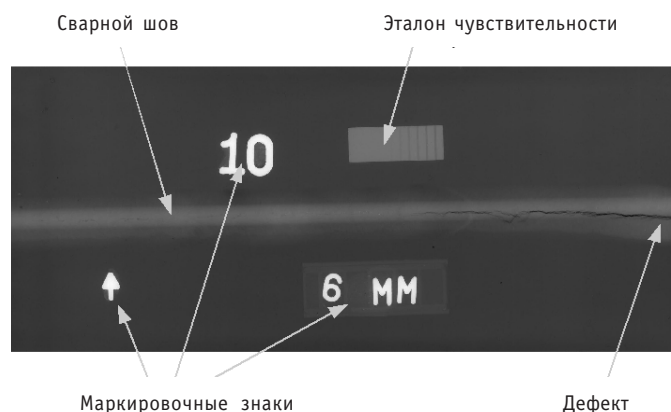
Пример радиографического снимка стыкового сварного соединения
